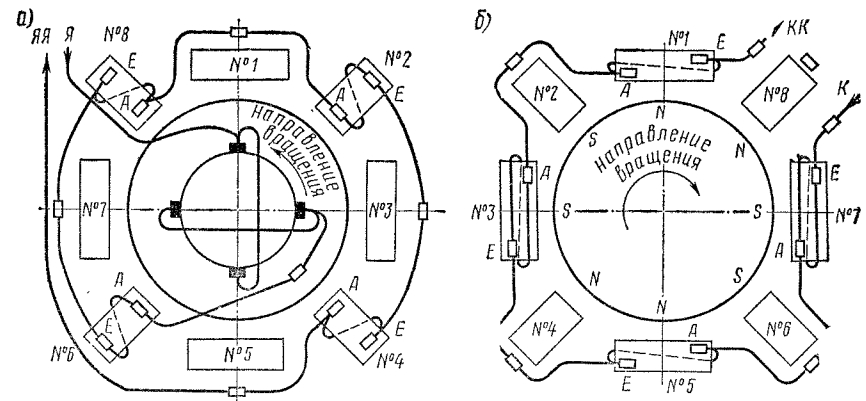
Схема соединения обмоток тягового двигателя НБ-406 со стороны коллектора (а) и противоположной стороны (б)
